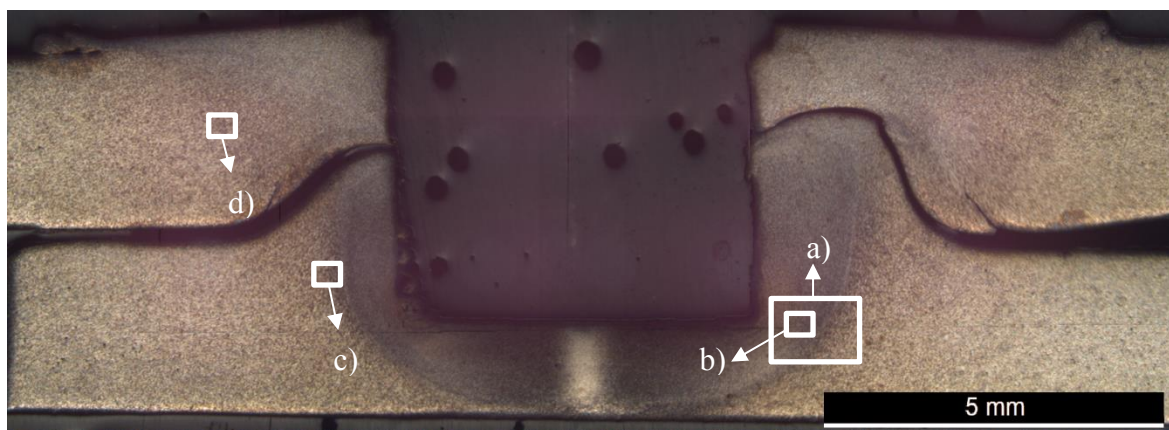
Macrografia do perfil de soldadura do provete S500B-3.
